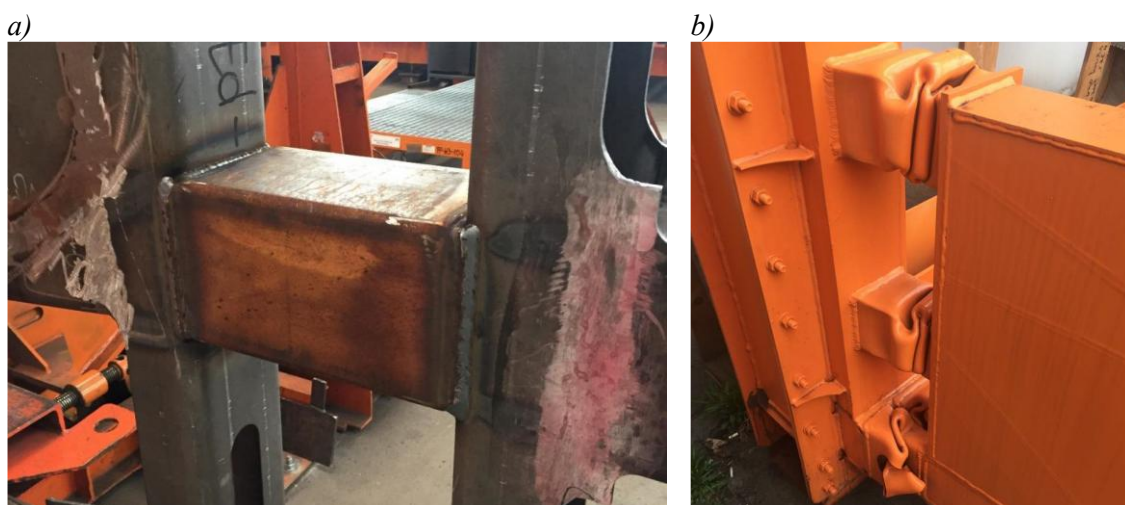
Plaster miodu zamontowany w pojazdach PesaDART [90]
